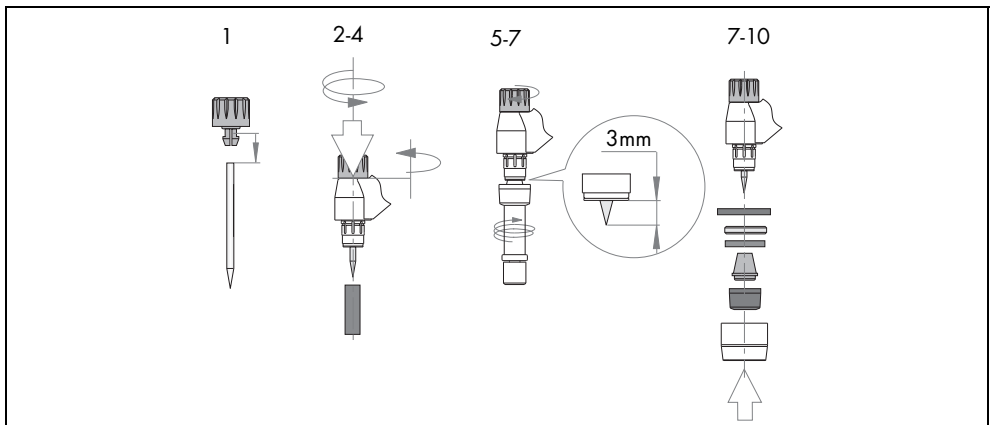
Handlungsschritte Brennerkörper ABIPLAS® WELD 250 MT ausrüsten
